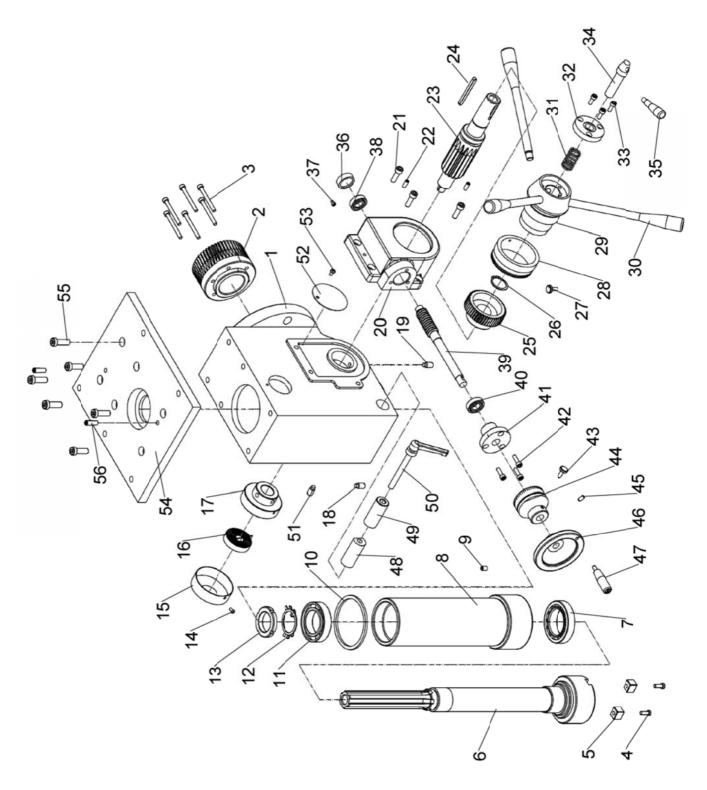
Universal Schwenkkopf - Universal swiveling head
